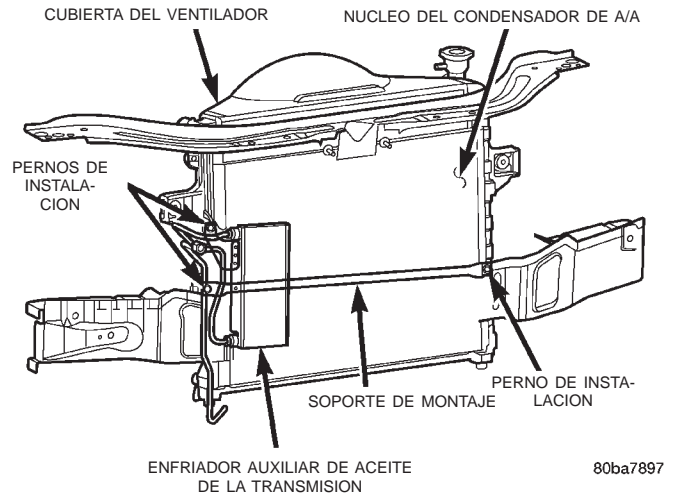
Soportes de montaje del enfriador de aceite—característicos
